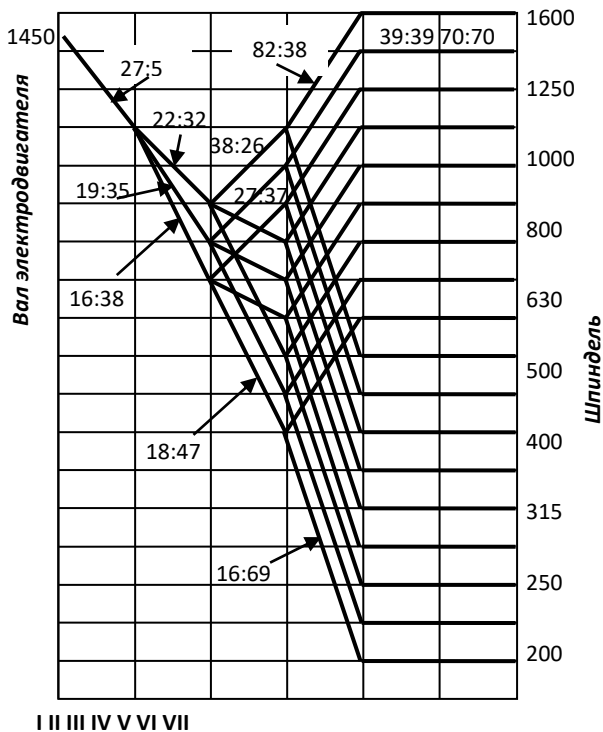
Картина частот оборотов главного привода станка 6М13ГН1
